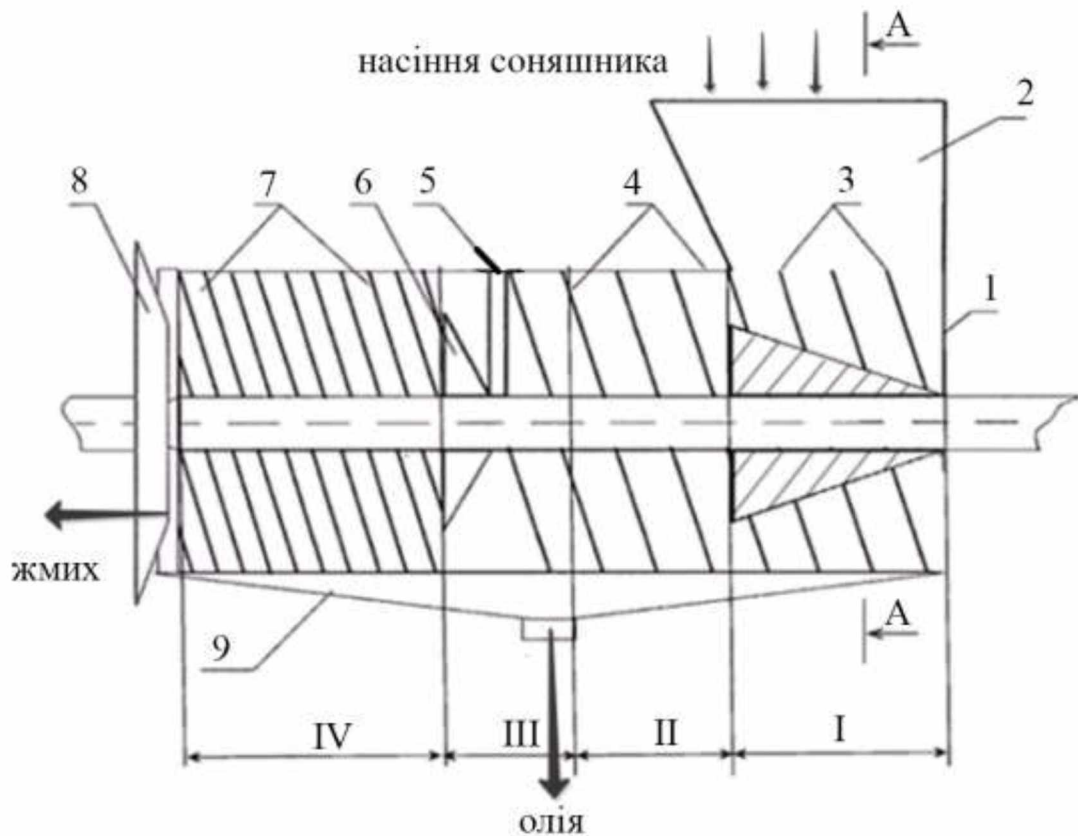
Конструктивно-технологічна схема двозахідного шнекового преса: 1 - корпус; 2 - завантажувальний бункер; 3 - подавальний шнек; 4 - пресувальний шнек; 5 - розпушувач мезги; 6 - конусна напрямна втулка; 7 - шнек; 8 - регулятор тиску; 9 - маслозбірник; I - зона завантаження матеріалу, II - зона стиснення, III - зона стабілізації тиску, IV - зона інтенсивного стиснення
